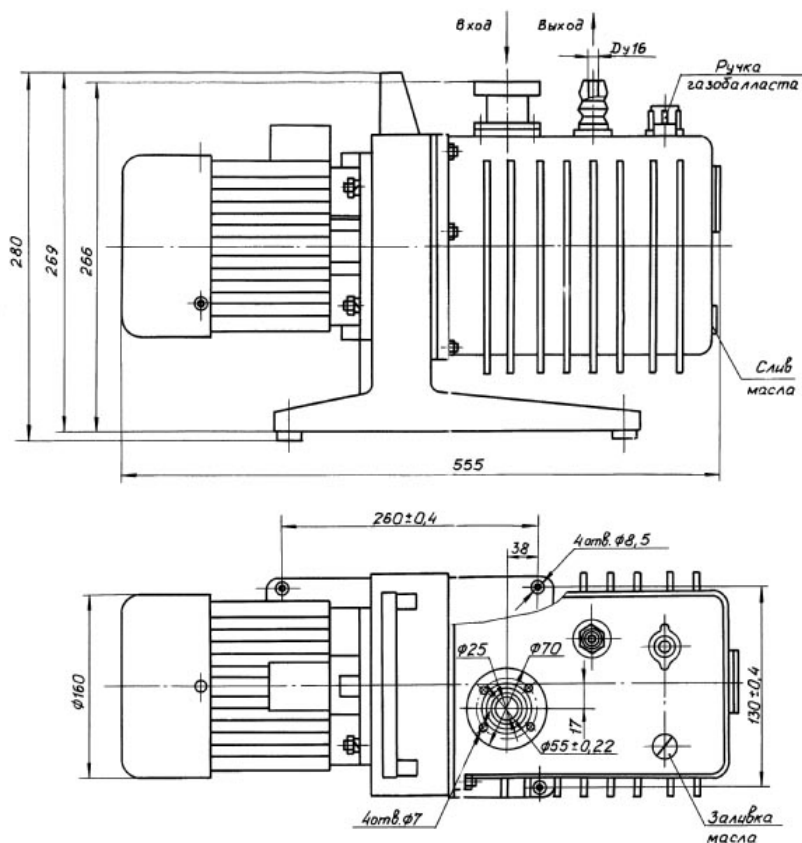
Габаритный чертёж насоса 2НВР-5ДМ
